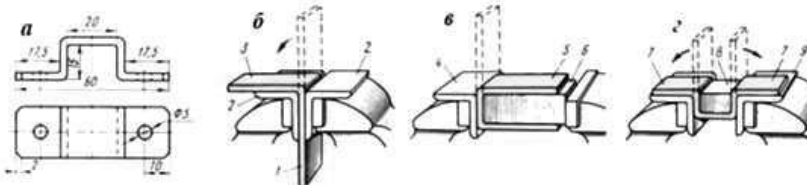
Виготовлення скоби зі смугової сталі: а – готова деталь; б – загин першої опори; в – загин другої опори; г – згинання скоби.
